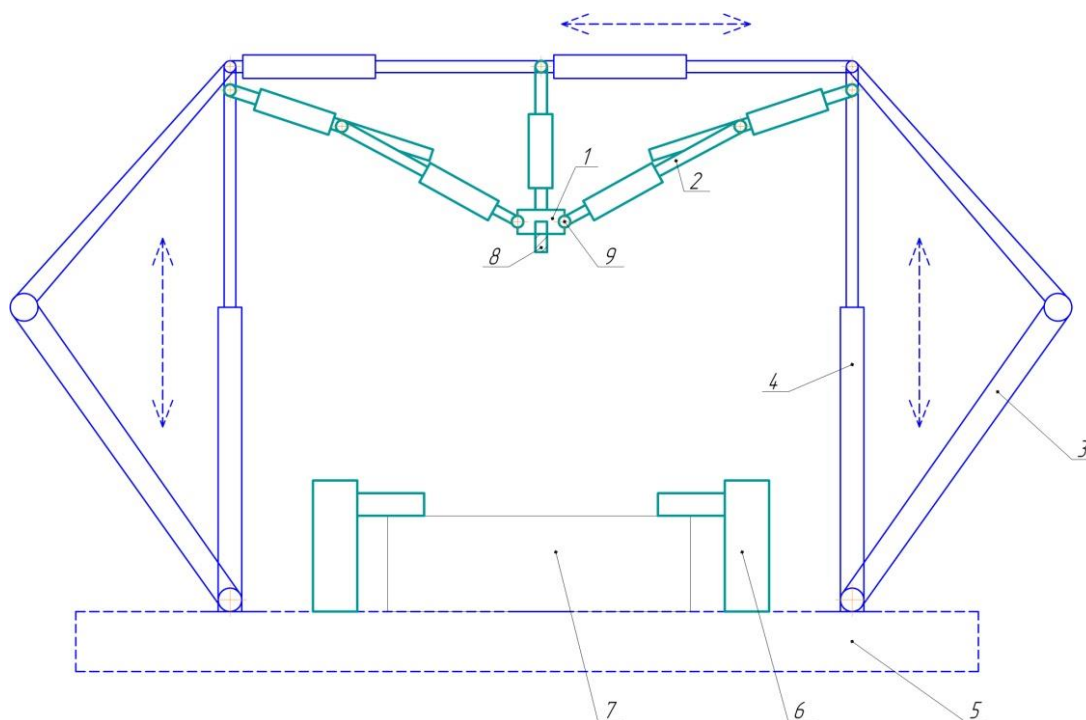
Рама для обработки деталей типа «Корпус подшипника»
